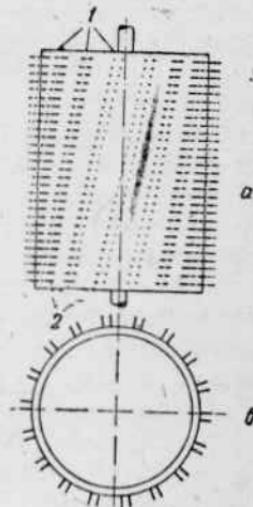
Схема расположения подвижных* шипов на барабане дробилки (а — план; б — разрез):
